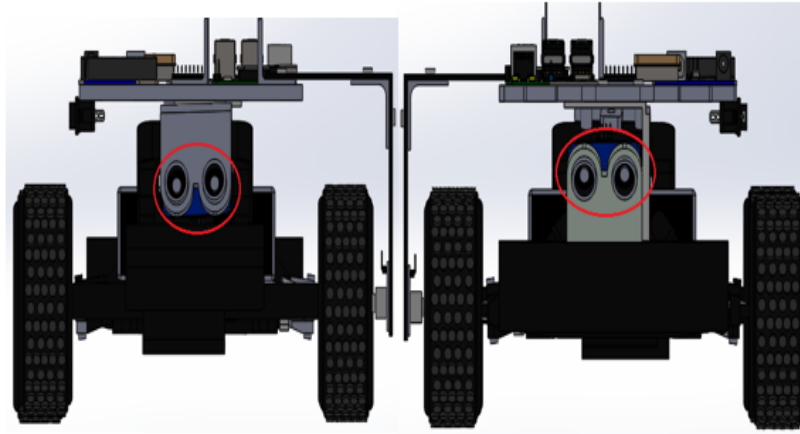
Sensor ultrasónico, parte frontal (lado derecho) y parte trasera (lado izquierdo) en CAD
